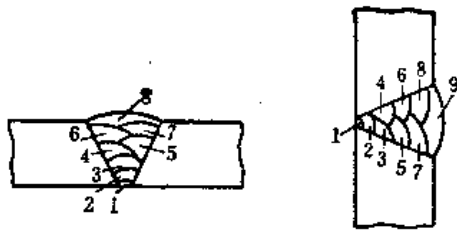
Cr25Ni20钢多层焊接顺序
